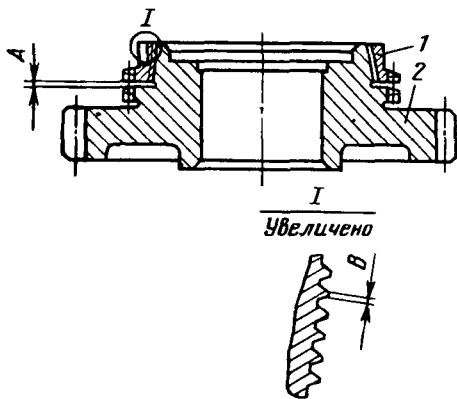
Замер зазора между торцами венца шестерни и кольцом синхронизатора:
